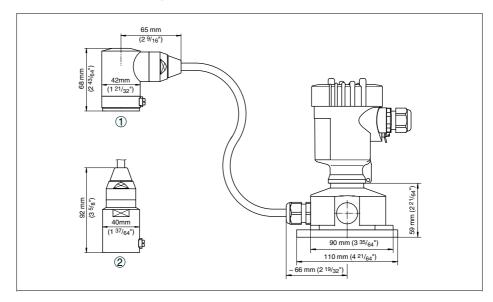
IP 68-Ausführung mit externem Gehäuse
